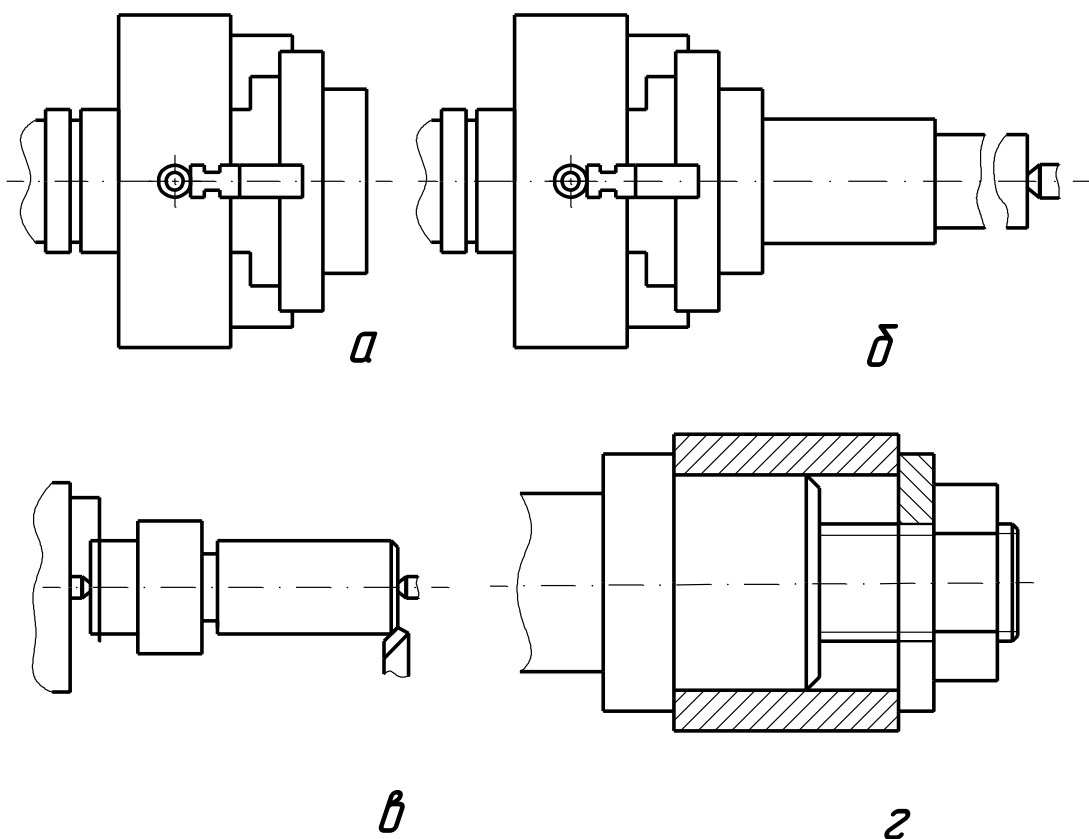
Способи закріплення заготовок на токарно-гвинторізних верстатах
